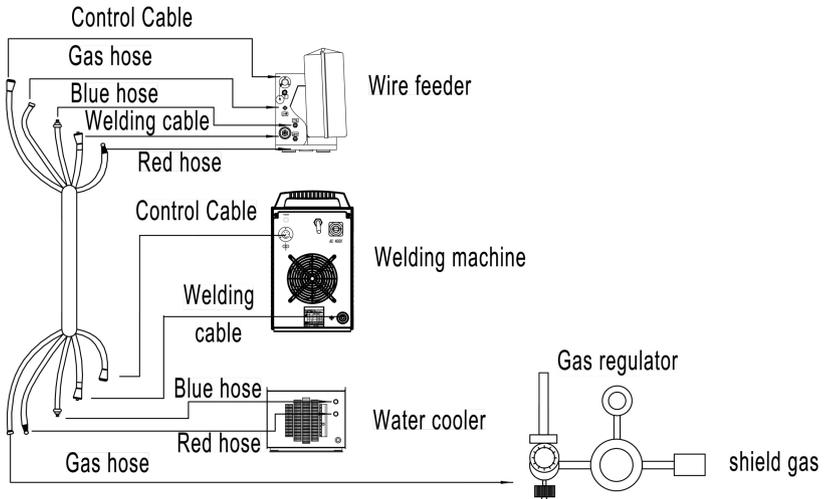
Conjunto de componentes del cable de soldadura
